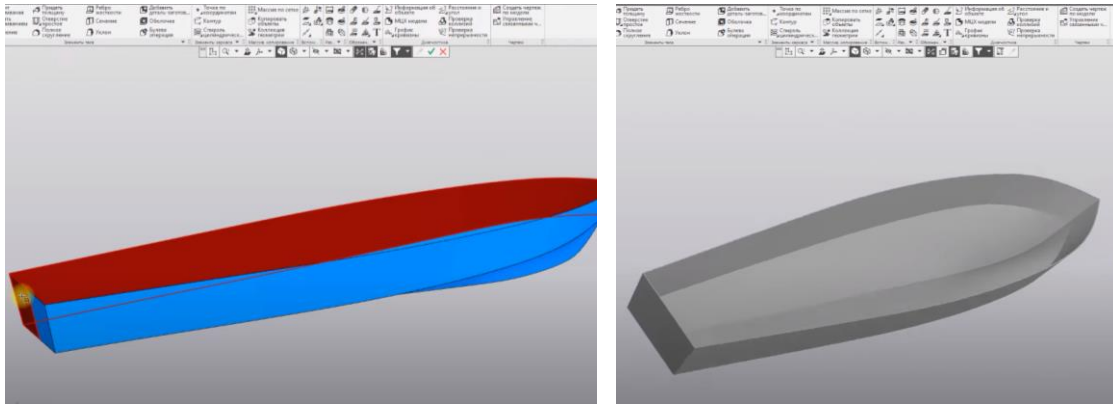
«Сшивка поверхностей» и законченная модель корпуса судна.
